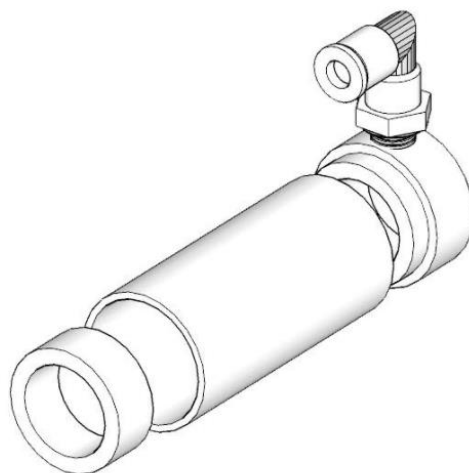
Sistema puesto a punto para dar inicio a la soldadura.
